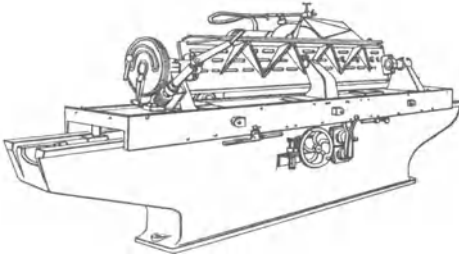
Scharfschleifmaschine für Langmesser. a Messer-Aufspannbalken; b Schneckengetriebe zum Einschwenken von a in den vorgeschriebenen Watenwinkel; c zu schleifendes Messer; d Schleifring oder Segment-Schleifzylinder.
